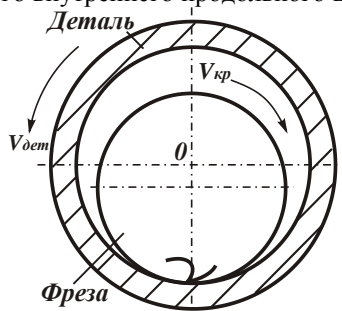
Схема фрезерования отверстия концевой фрезой.
